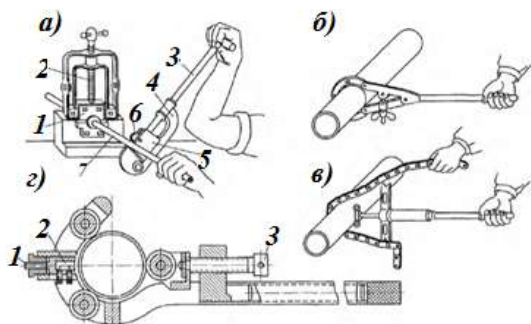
Труборезы: а - роликовый: 1 - прижим; 2 - винт; 3 - винтовой рычаг; 4 - скоба; 5 - кронштейн; б - режущие ролики; 7 - труба; б - хомутовый; в - цепной: г - резцовый: 1 - нажимной винт; 2 - отрезной резец; 3 - винт;
